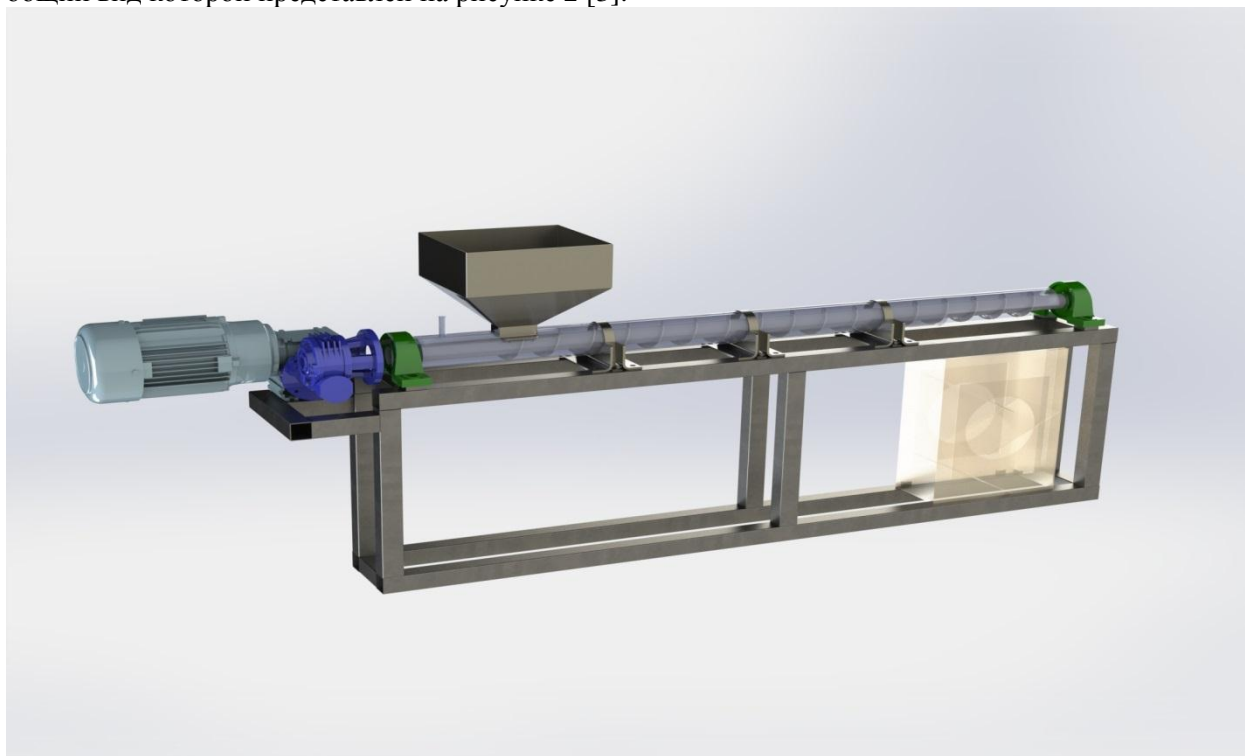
Общий вид устройства для гидротермической обработки зерна овса
